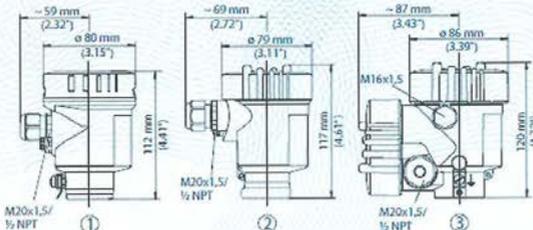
Корпус із нержавіючої сталі (1 – однокамерний корпус, електрополірований; 2 – однокамерний корпус, точне лиття; 3 – двохкамерний корпус, точне лиття)
